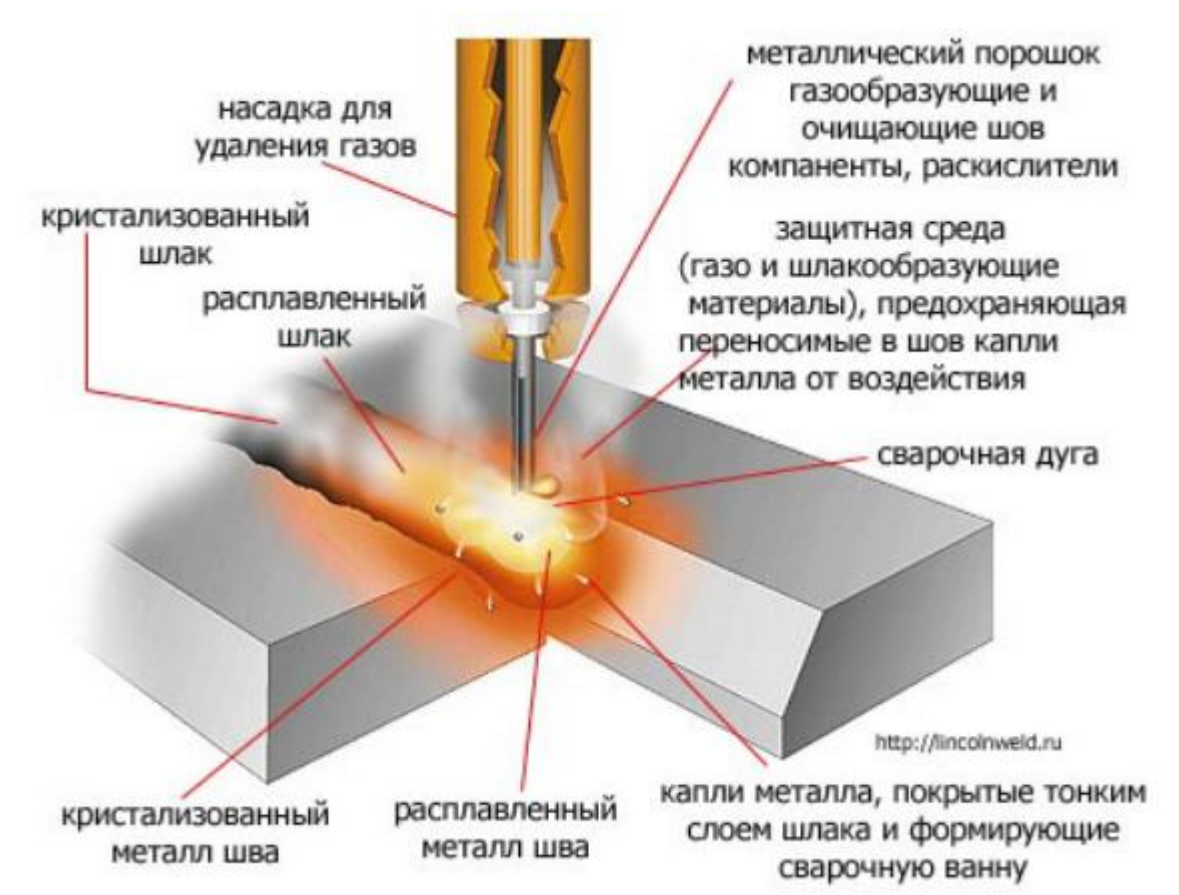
Сварка порошковой проволокой [24]
